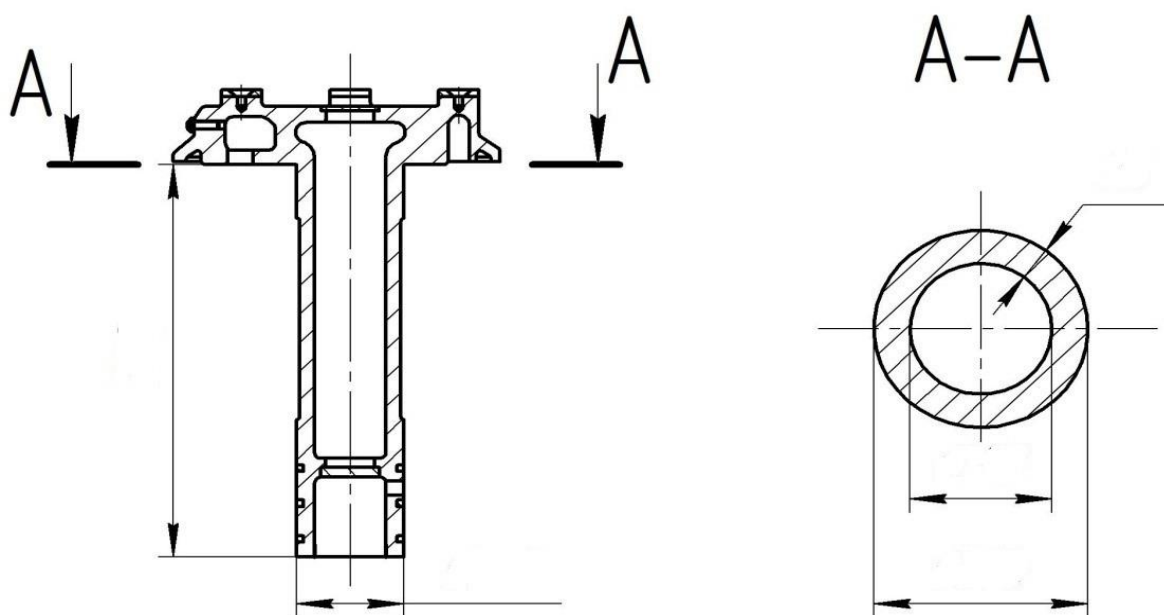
Небезпечний переріз струшувального механізму формувальної машини.
